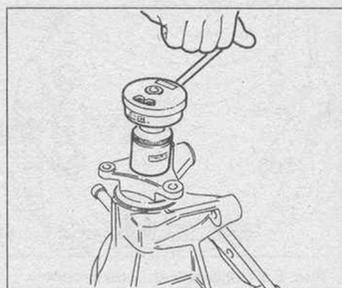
Проверка крутящего момента шестерни механизма конечной передачи (Глава 6)
